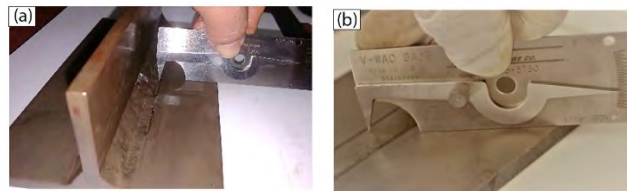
Disposición V-WAC Gauge para dimensionar el tamaño de (a) socavado y (b) refuerzo en junta a tope
